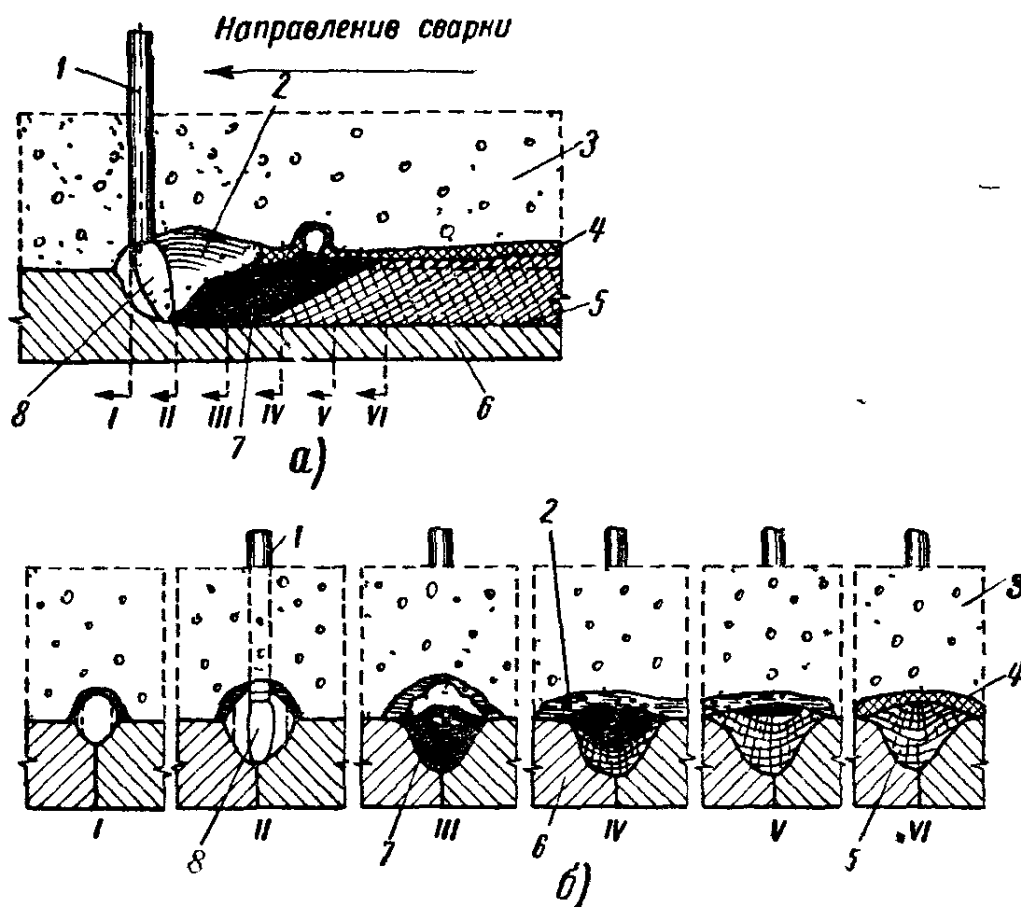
Схема горения дуги и образование металла шва при сварке под флюсом:
